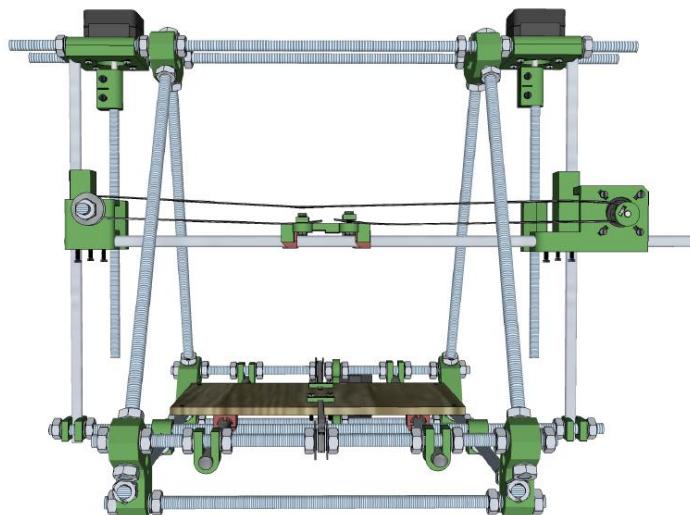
Ensamblado completo del eje X. Terminado (cuerpo casi acabado)
